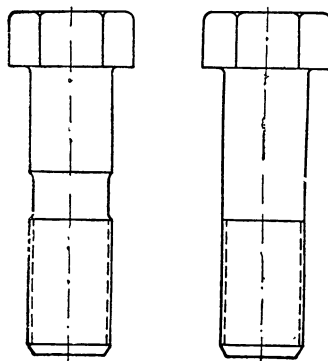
а. Болт крепления добавочного полюса электродвигателя ЭДТ-200Б. Слева — новая конструкция; справа — старая конструкция
